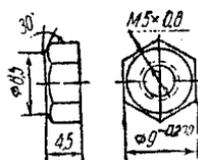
Дет. № 3076. Гайка к винту заглушки корпуса секции насоса
